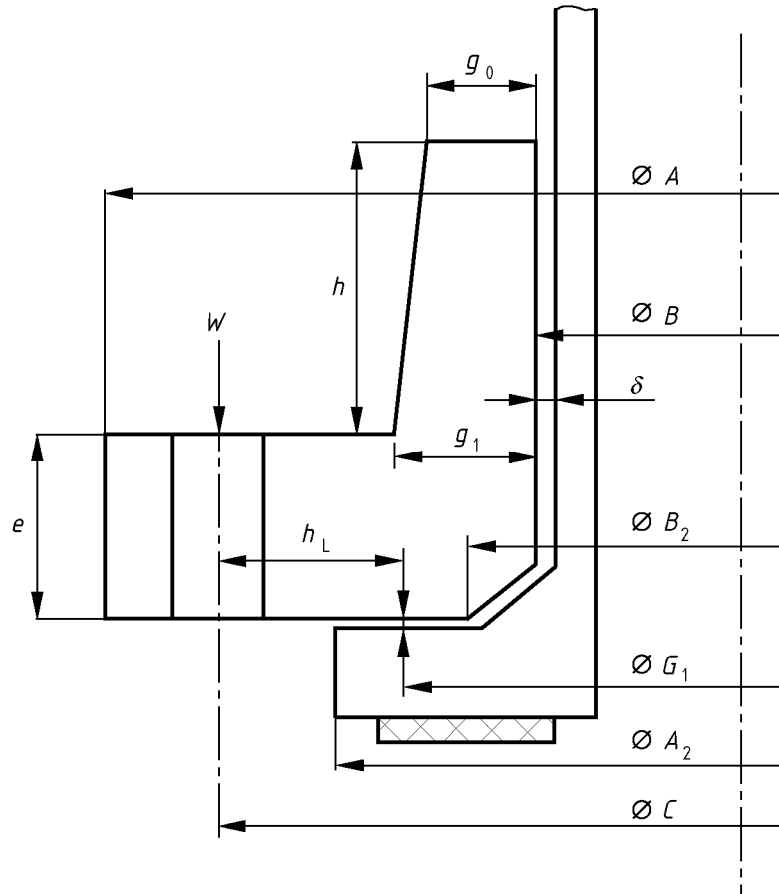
Junta del tipo de solapa; brida suelta con cubo
